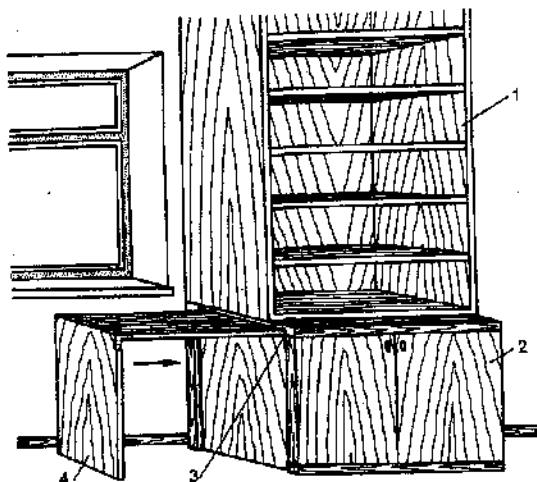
Выдвижной стол; 1 — книжный шкаф; 2 — тумба под шкаф; 3 — паз для захода крышки стола; 4 — опорная боковина
